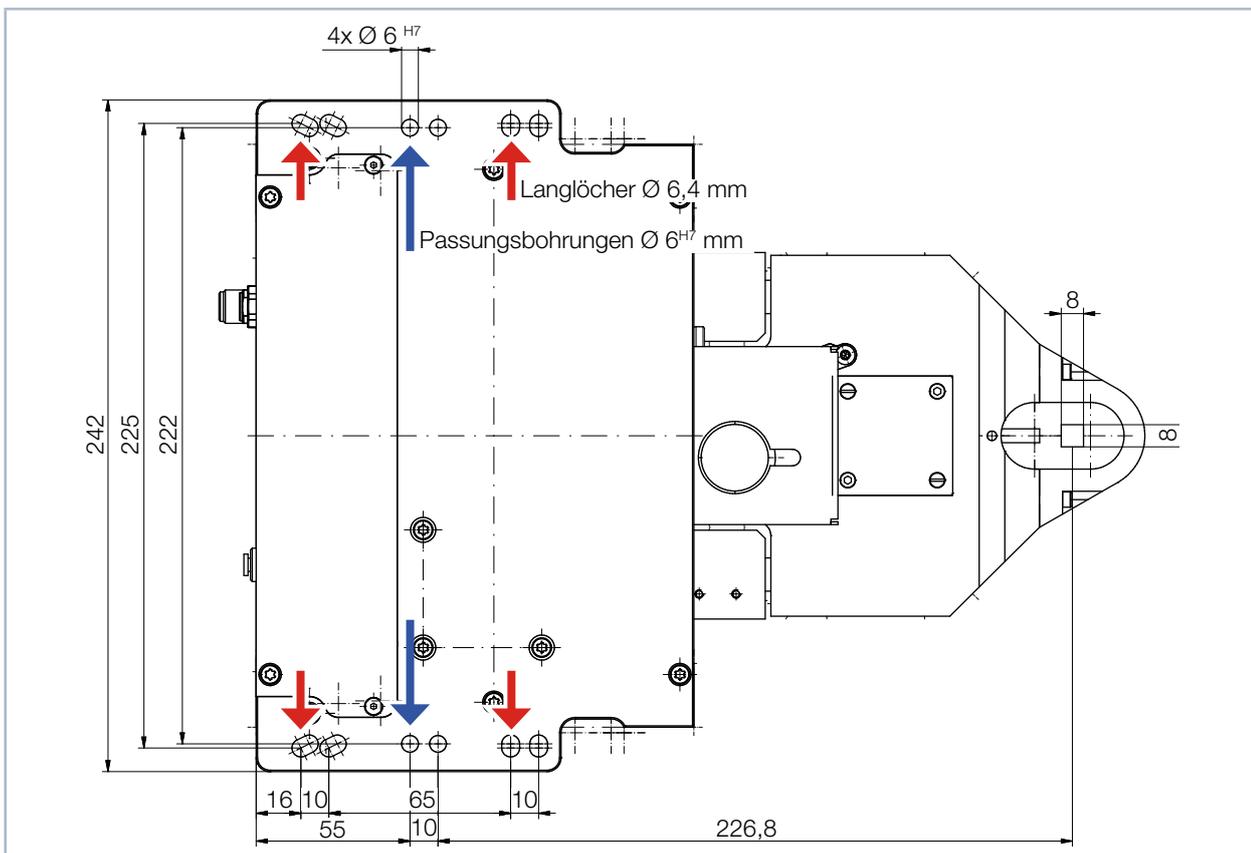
Befestigungsbohrungen, Ansicht von oben (gleiches Bohrbild unten)
